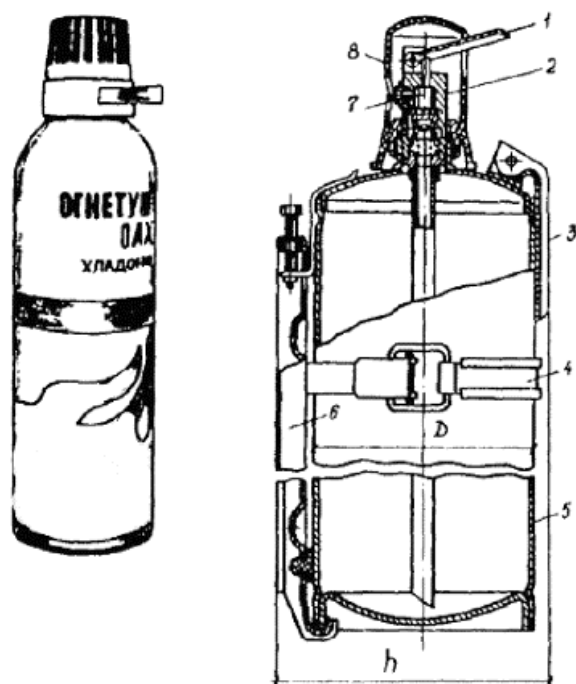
Хладоновый огнетушитель ОУБ-3А (ОУБ-7А): 1 – пусковой рычаг; 2 – запорная головка; 3 – рукоятка; 4 – крепление; 5 – баллон; 6 – кронштейн; 7 – распылительное устройство; 8 – предохранительный колпак
